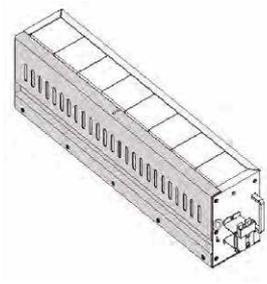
Instalación de baterías 4: instale la cubierta izquierda
